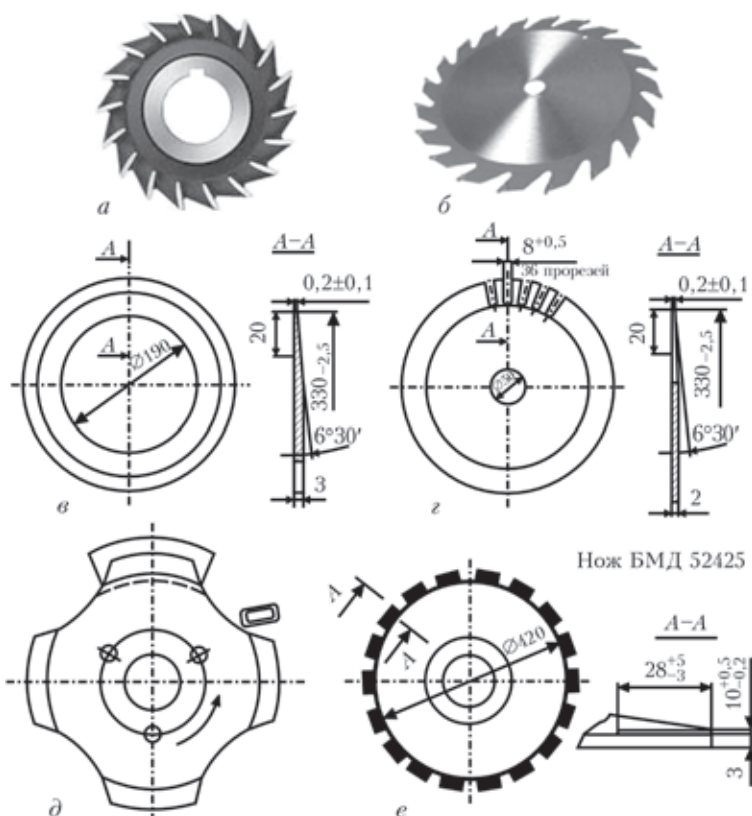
Тонкие диски, подлежащие наплавке: а — дисковая фреза; б — дисковая пила; в, г — соответственно не приводной и приводной диски для резки шифера; д — нож для среза подсолнуха; е — нож-ботворез БМД 52425
